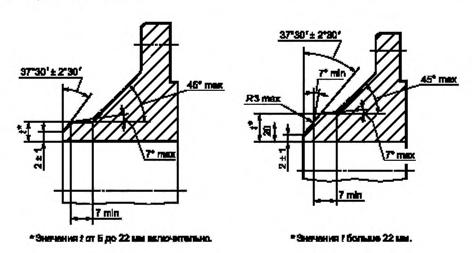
Разделка кромки под сварку для фланцев типа 11, ряд 2
